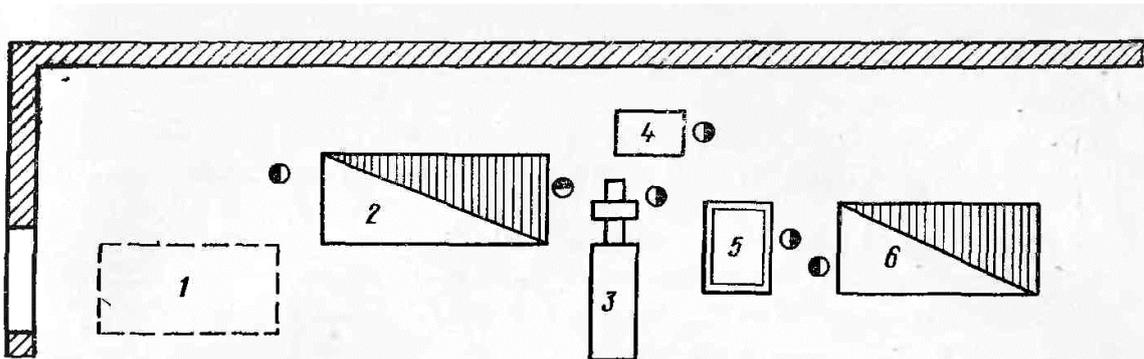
Схема расположения оборудования на участке изготовления пружин: 1 — стеллаж для заготовок; 2 — нагревательная печь; 3 — станок для навивки пружин; 4 — плита для регулировки шага витков; 5 — закалочная ванна; 6 — печь отжига
